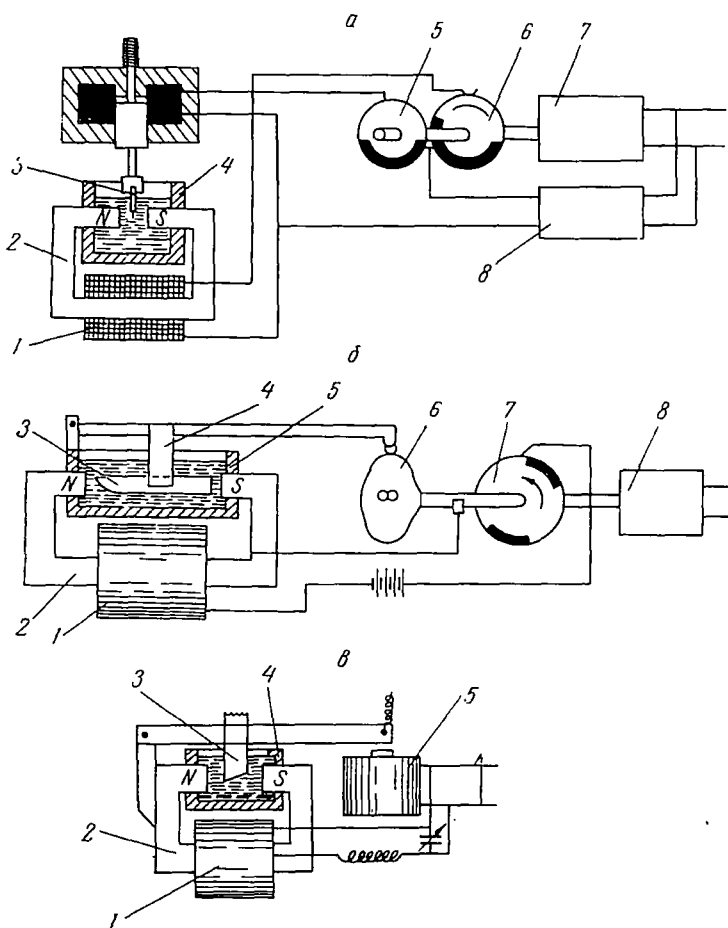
Схемы устройств для полирования и заточки режущего инструмента
